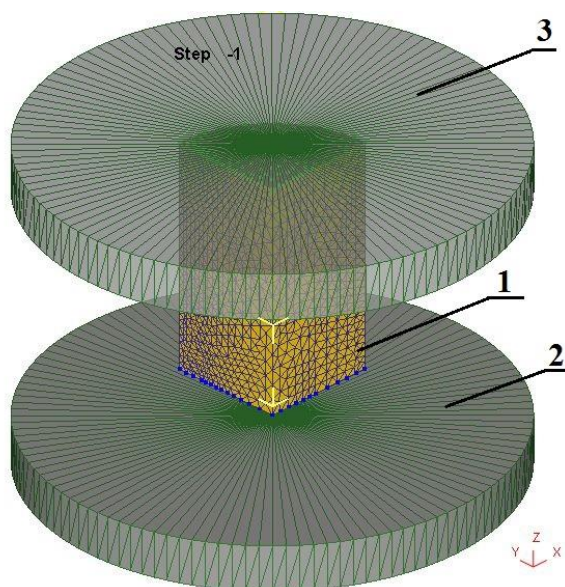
Схема нагружения с сеткой конечных элементов: 1 – цилиндрическая заготовка (четверть объема); 2 – плита пресса; 3 – осаживающая плита
